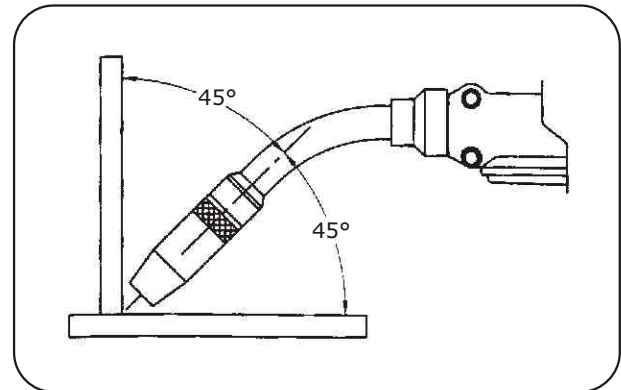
Elektrod Açısının ve Kaynak Tekniğinin Etkileri
